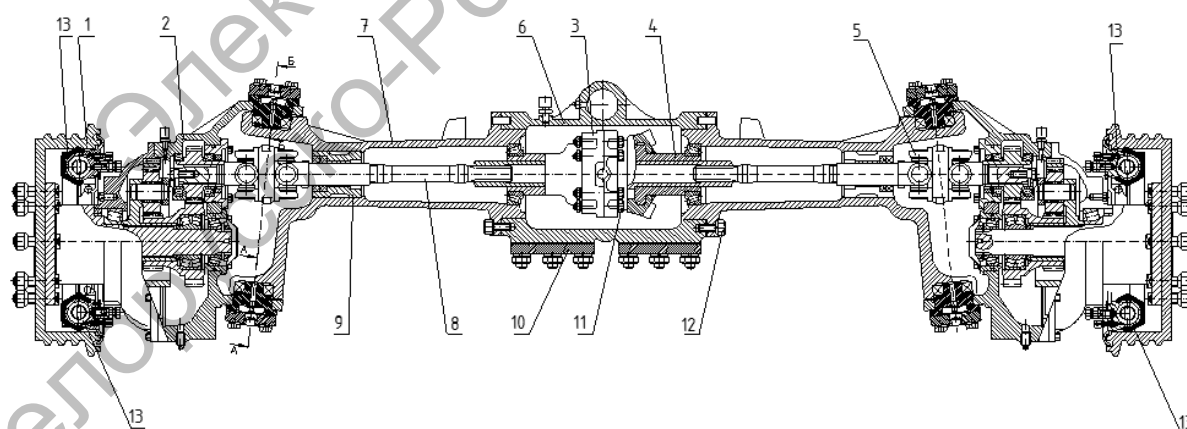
Тормозной механизм передних ведущих колес трактора с неподвижными опорами:
